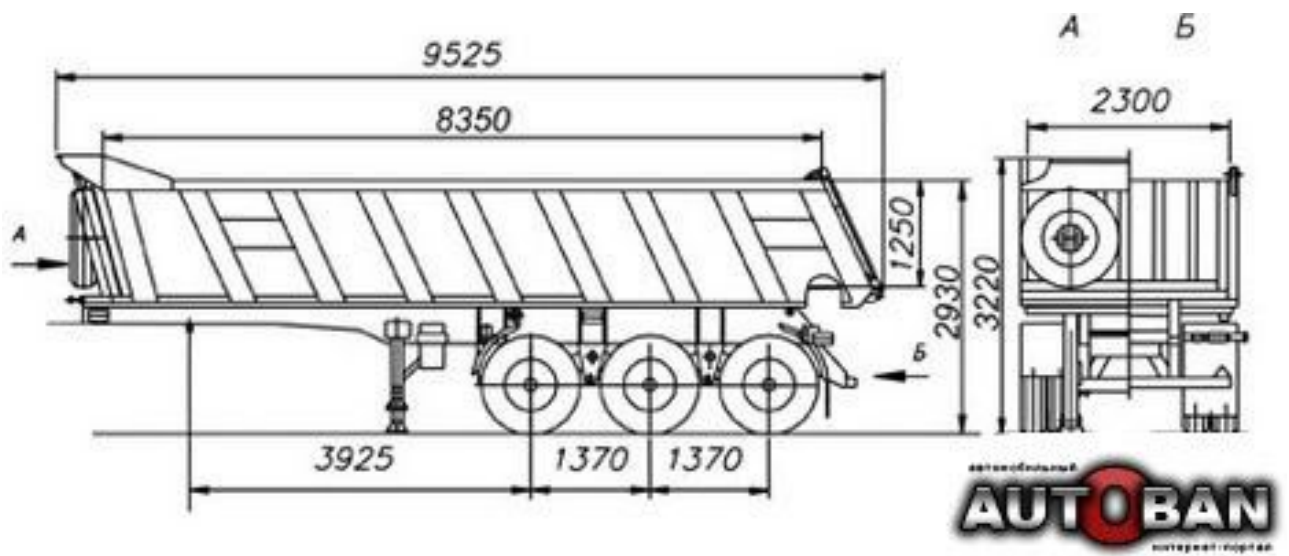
В - Самосвальный полуприцеп МАЗ-950600-020
